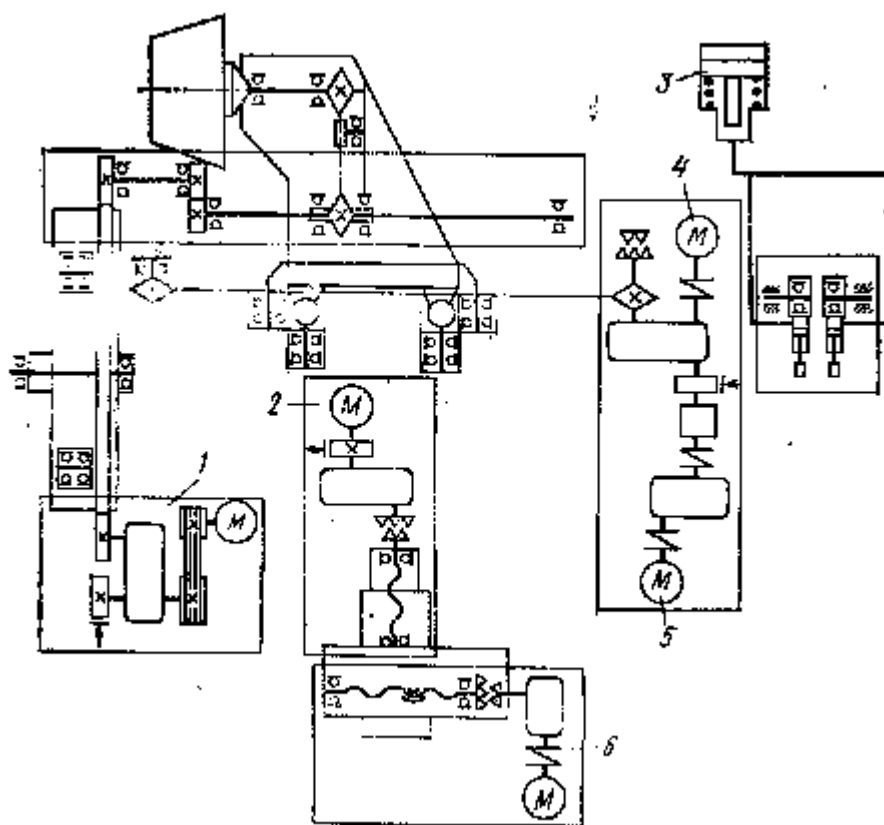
Кинематическая схема установки СМЖ-117А:
